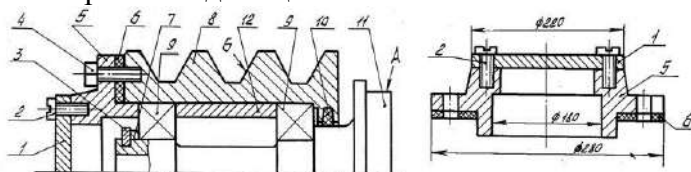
Эскиз сборочной единицы (Сб.11 – Ступица)
